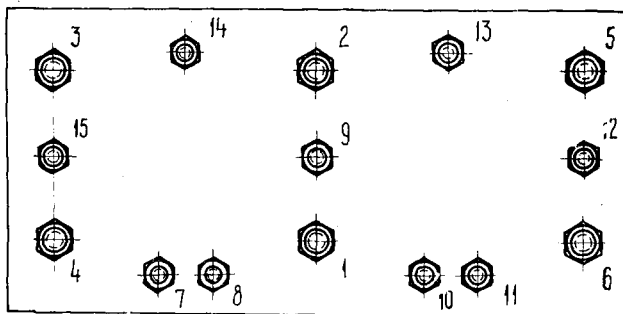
Схема затяжки гаек крепления головки цилиндров
